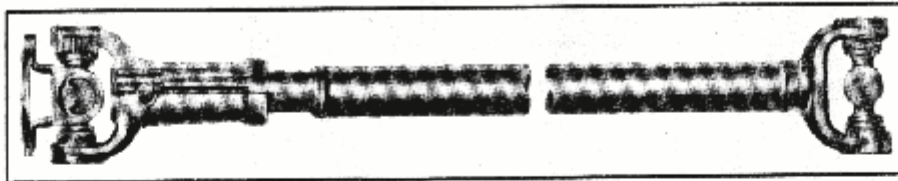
CONJUNTO DO EIXO CARDÃ
